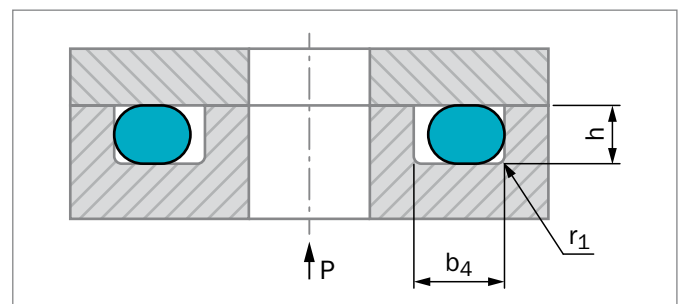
Axialer Einbau, statisch, bei Innendruck
